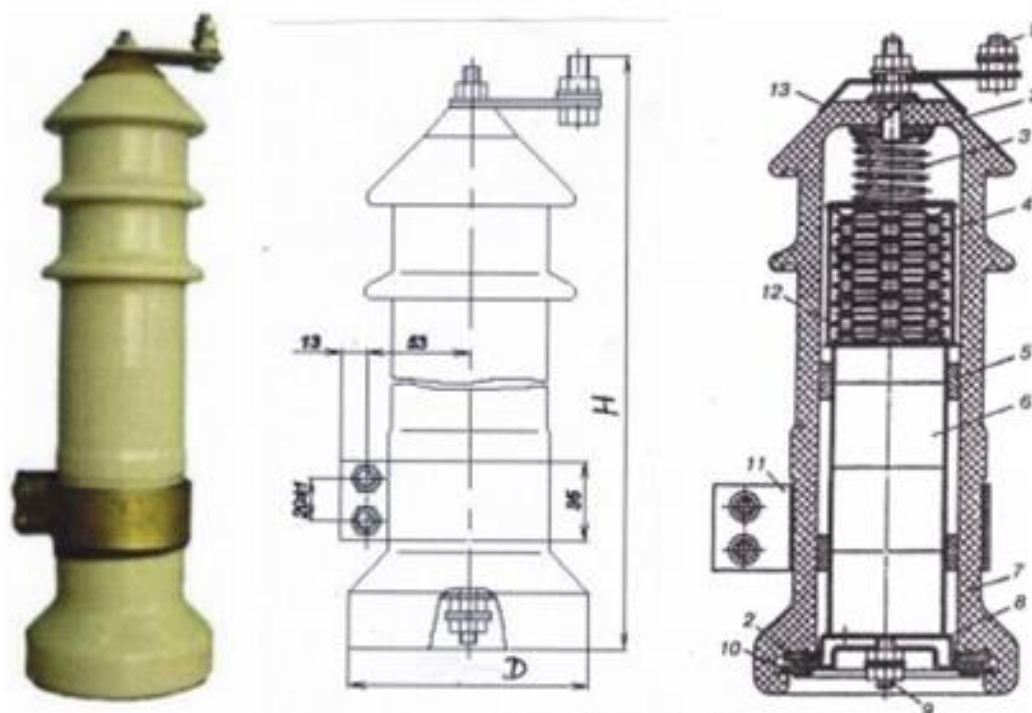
Внешний вид и конструктивная схема вентильного разрядника РВО-10
